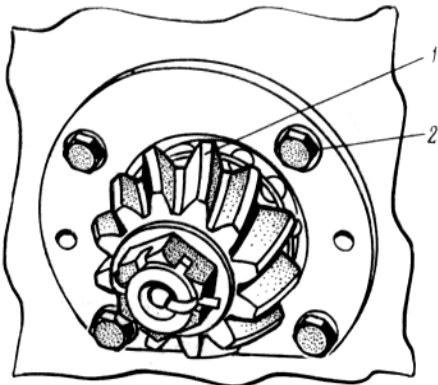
Знімання ведучої шестерні головної передачі: 1- ведуча шестерня; 2- болт
